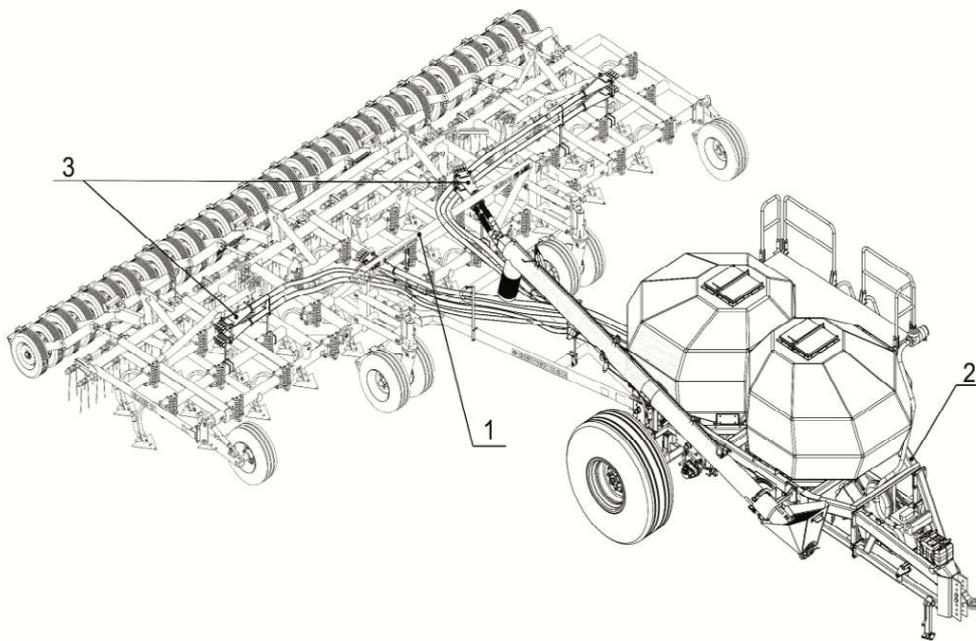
Сівалка-культиватор пневматична широкозахватна
